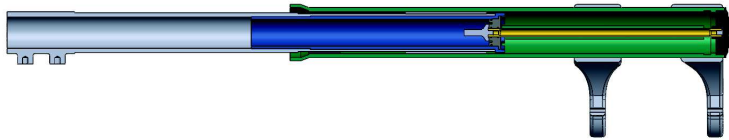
Modelo simplificado para el ensayo de tracción. Vista de sección.
